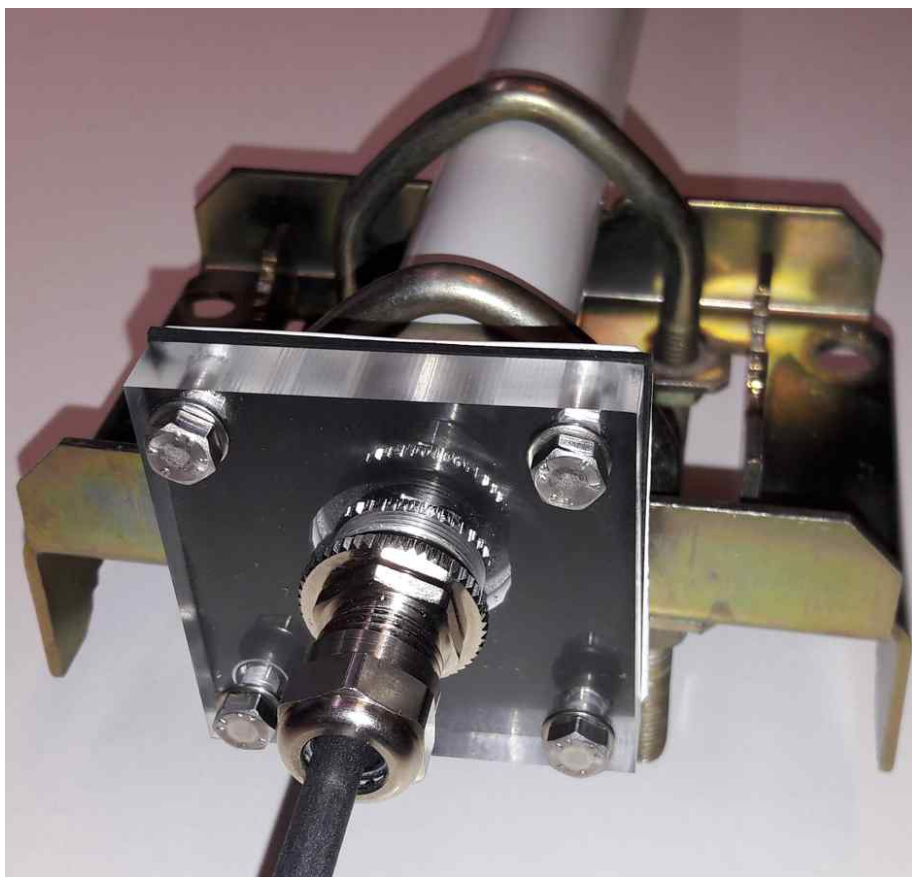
Embase du mât équipée de la platine d'étanchéité
